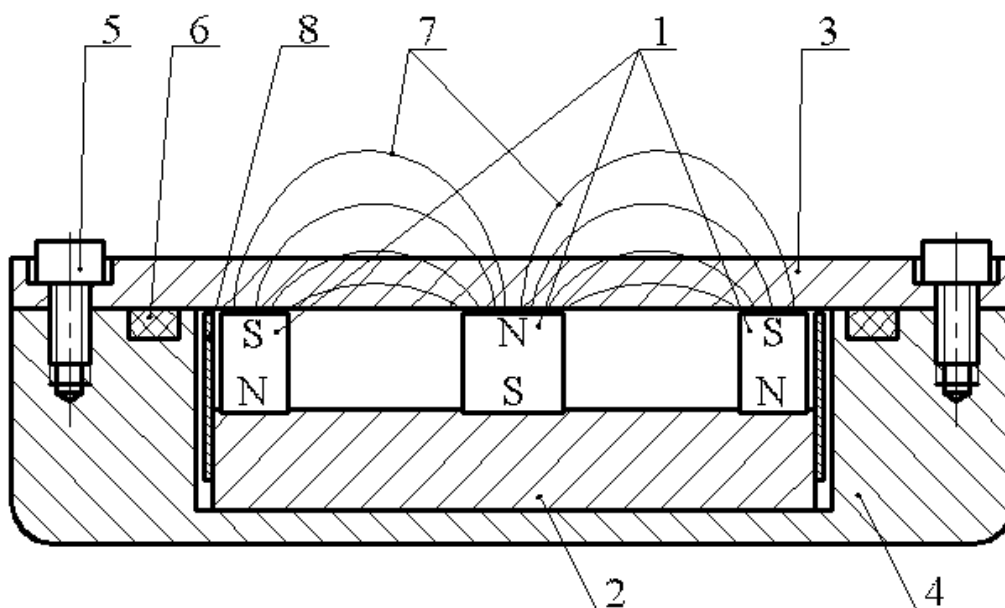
Поперечный разрез магнетрона: 1-магниты; 2-магнитопровод; 3- мишень; 4-корпус; 5-винты крепления мишени; 6-резиновое уплотнение; 7-силовые линии магнитного поля; 8-магнитный шунт
